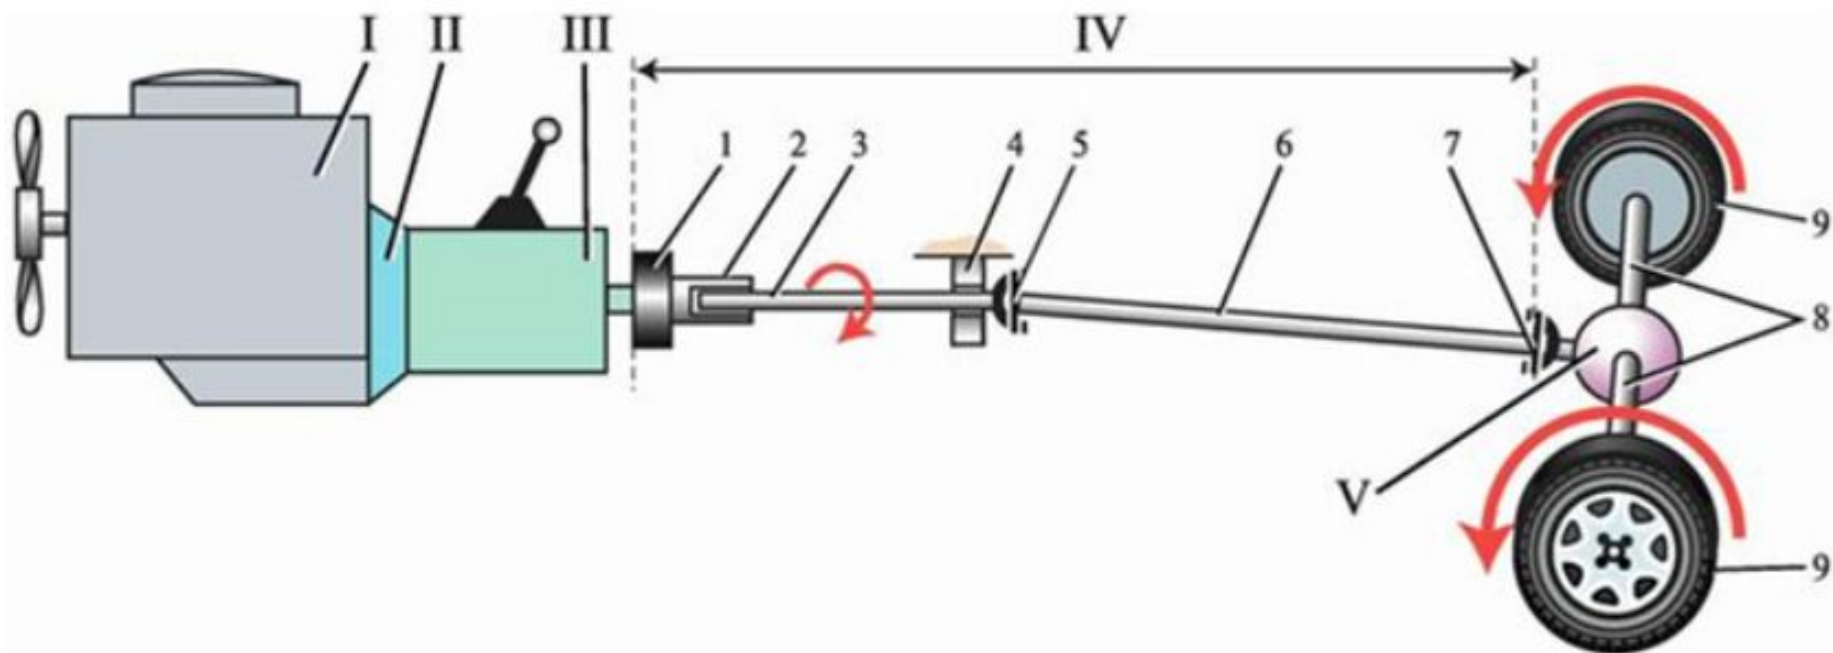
Схема трансмиссии заднеприводного автомобиля: I – Двигатель; II – Сцепление; III – Коробка передач; IV – Карданная передача: 1 – эластичная муфта; 2 – шлицевое соединение; 3 – передний карданный вал; 4 – подвесной подшипник; 5 – передний карданный шарнир; 6 – задний карданный вал; 7 – задний карданный шарнир; V – Задний мост с главной передачей и дифференциалом: 8 – полуоси; 9 – ведущие (задние) колеса
